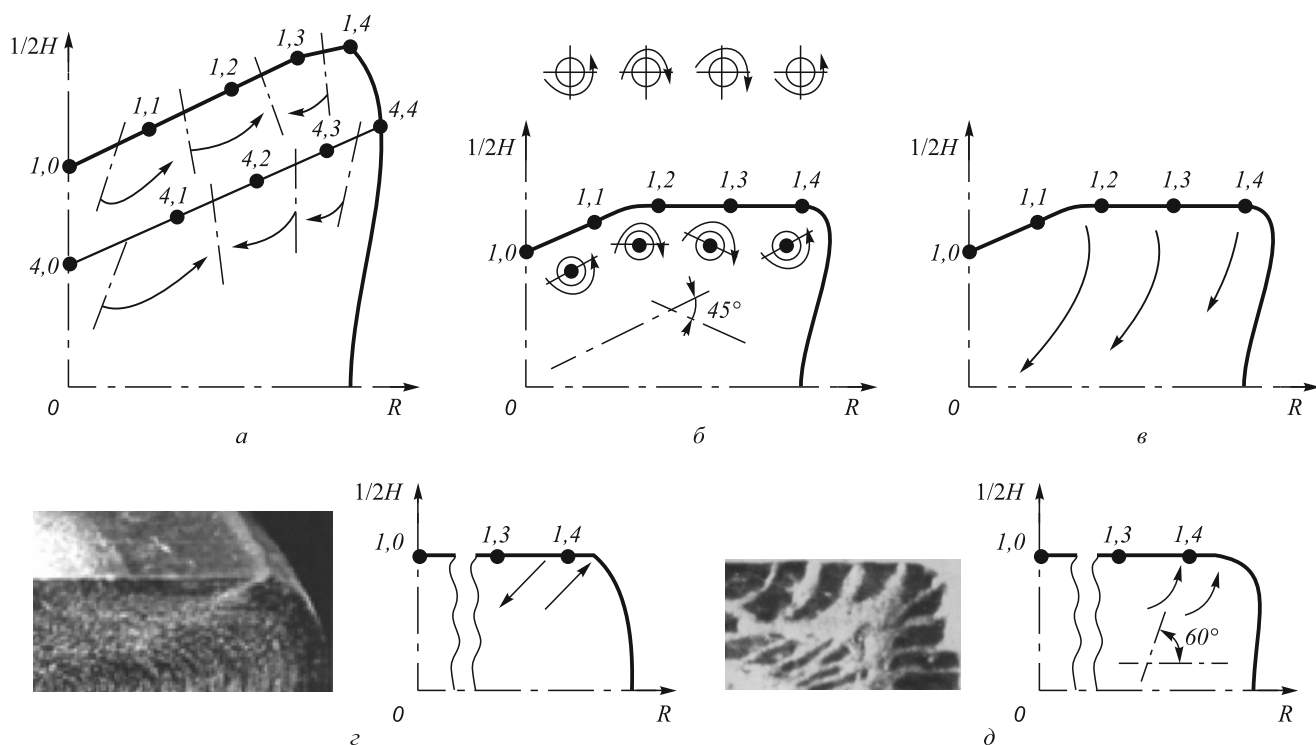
Фрагменты явлений на стадиях осадки заготовки коническими и плоскими бойками:
